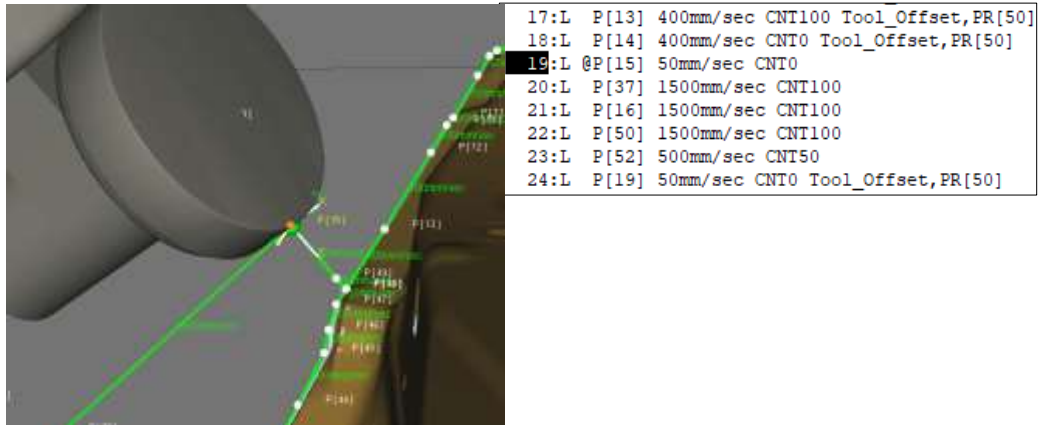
Robot C cambio de la zona de la pieza a engrapar [2]
